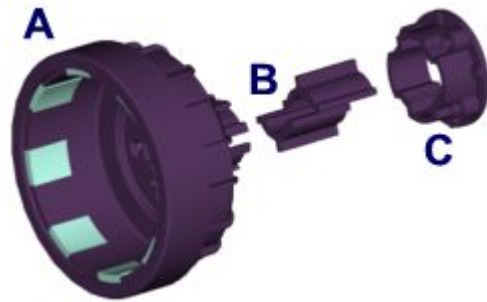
E – Entraînement magnétique complet – douille de serrage – collier de serrage
